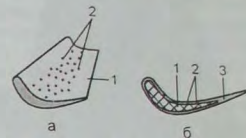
Общий вид керамического стержня (а) и профиль "пера" модели качественной турбинной лопатки: 1 — керамический стержень; 2 — гранулы; 3 — модель отливки
